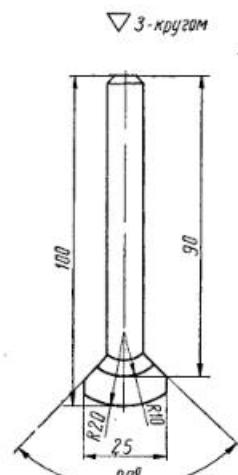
Шток для притирки клапанов двигателей типа NVD-48 и NVD-24.
